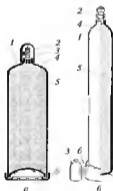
Ацетиленовые баллоны: а — сварной БАС-1-58. б — бесшовный; 1 — корпус, 2 — запорный вентиль, 3 — предохранительный колпак, 4 — газовая полушуга; 5 — пористая масса с ацетоном, 6 — оловянный башмак
